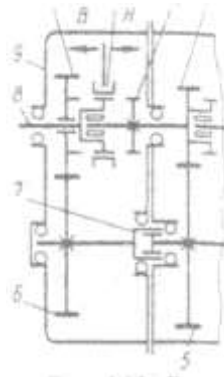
Схема додаткової коробки передач (подільника) (КамАЗ):
